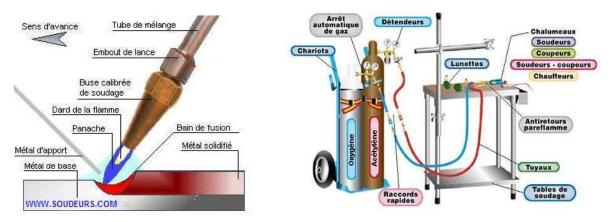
Principe de Soudage oxygaz et le croquis didactique du procédé de soudage a la flamme oxyacétylénique [17]
